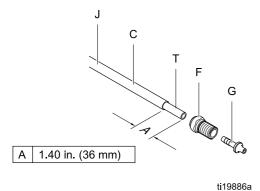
Dimensiones de la manguera sin carcasa 24M733 en la pistola
